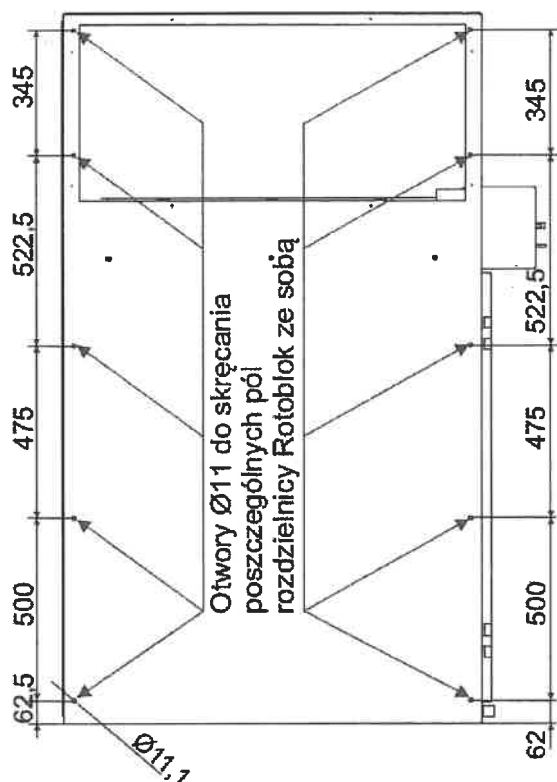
Montaż rozdzielnic Rotoblok do posadzki betonowej wariant bez ramy 1950 mm
